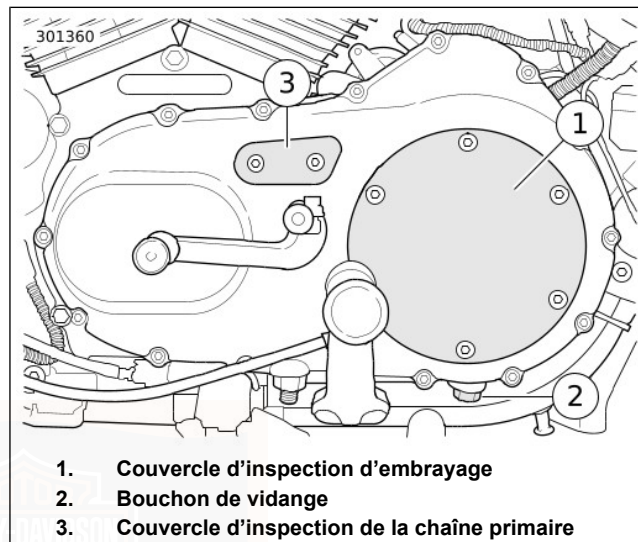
Couvercle primaire : Modèles Sportster (modèle XL illustré)
